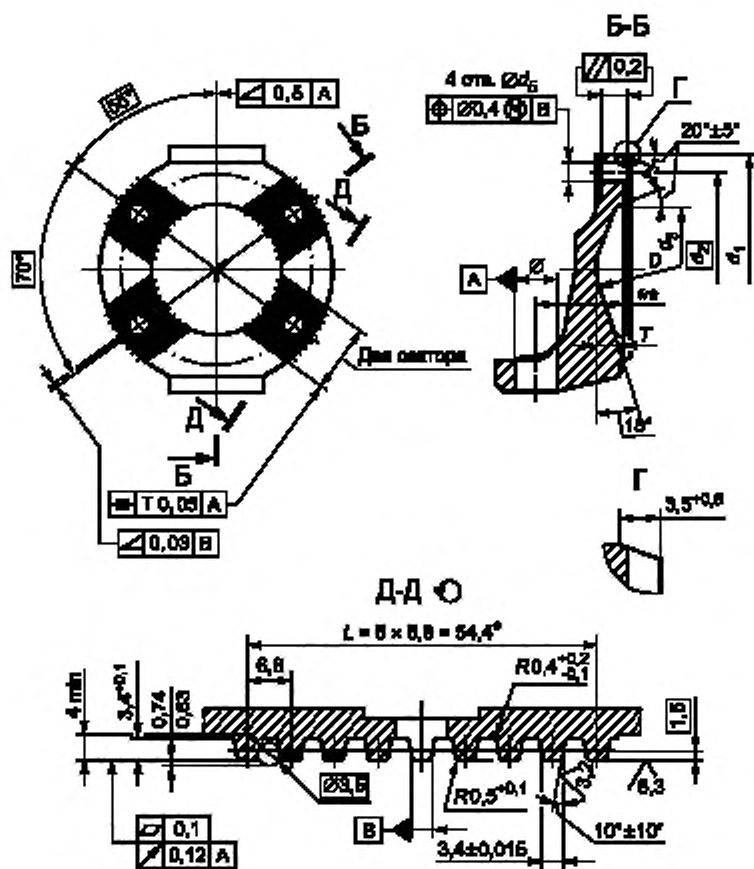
Типы фланцев-вилок карданных шарниров с присоединительными поверхностями
